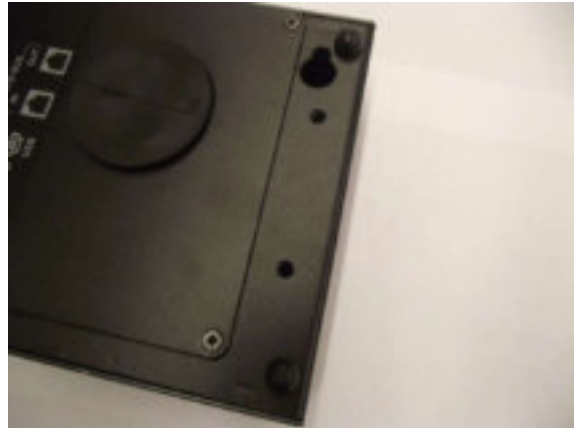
Gewindebohrungen Rückseite VAP-1 rechts
